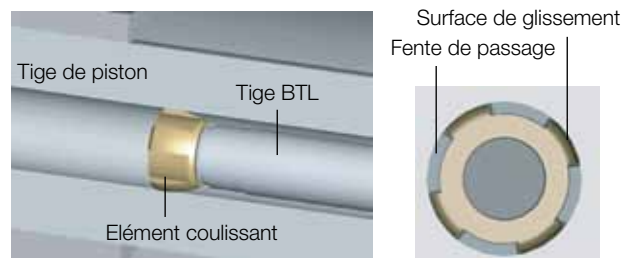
Vue détaillée et vue de dessus de l'élément coulissant
